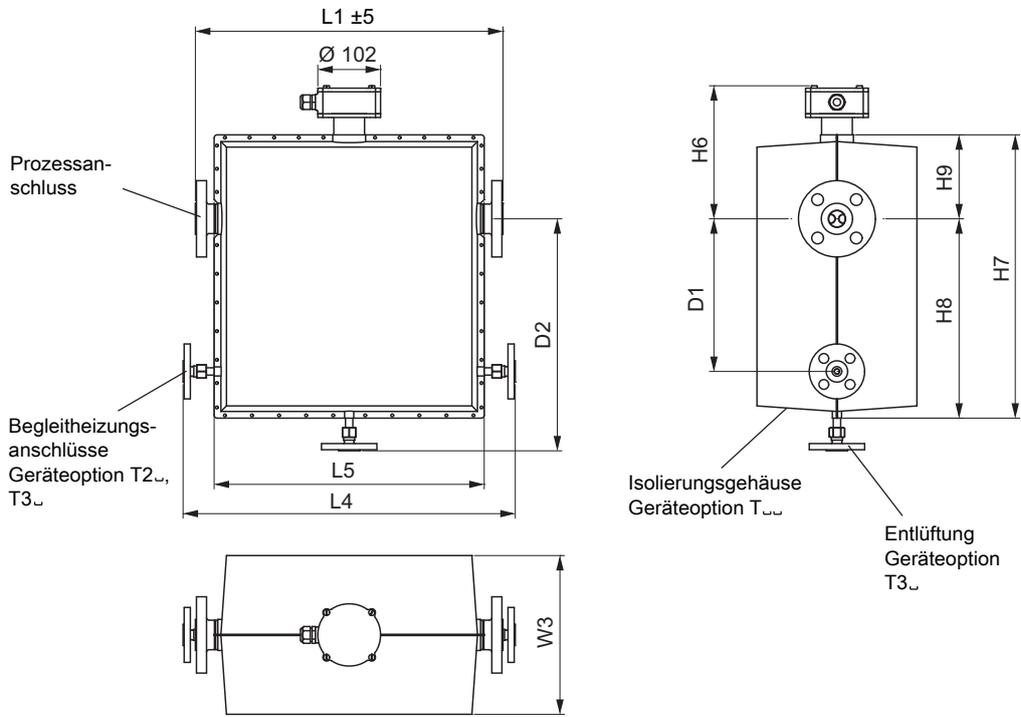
Abmessungen in mm: Variante mit Isolierungsgehäuse
